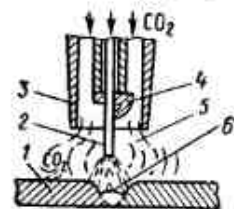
Схема дуговой сварки в среде углекислого газа:
